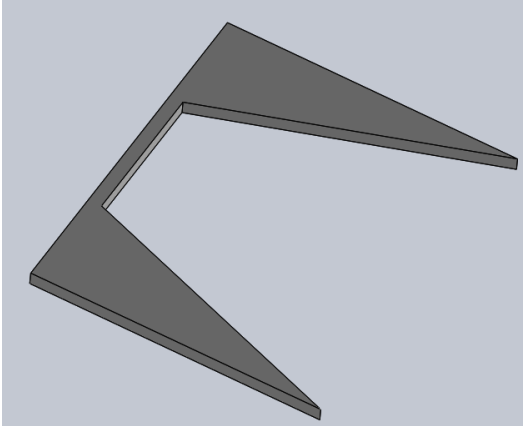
Chapa superior horizontal del conjunto cajón. [2]
